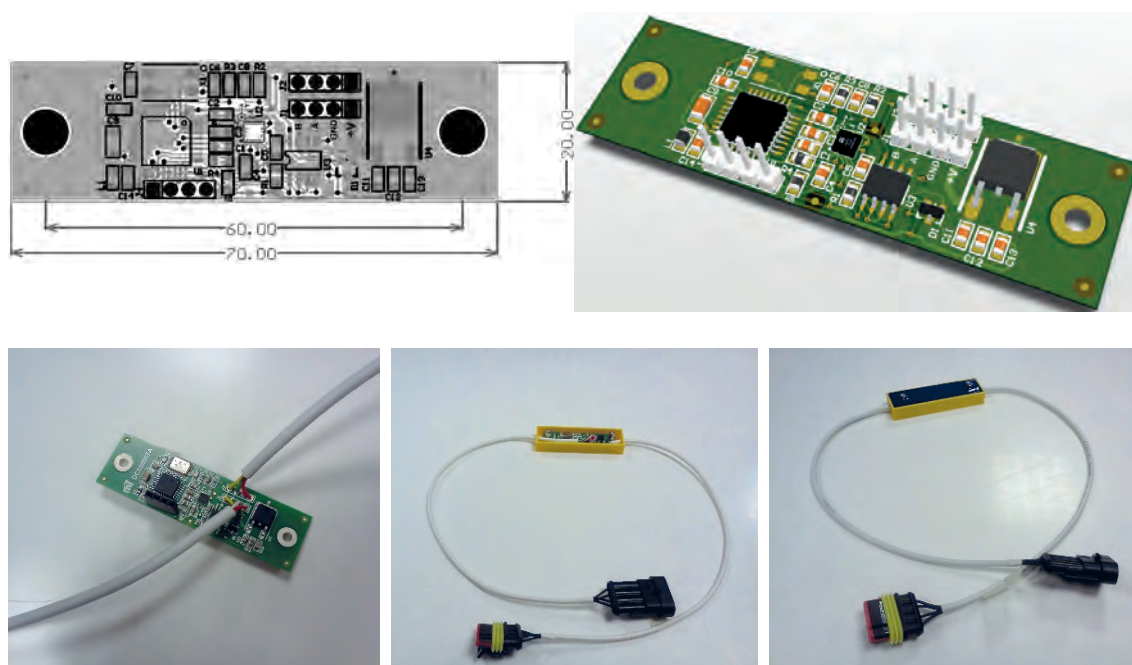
PCB con dimensioni, *rendering* 3D della scheda elettronica e foto della scheda alloggiata nel *box* elettronica.
